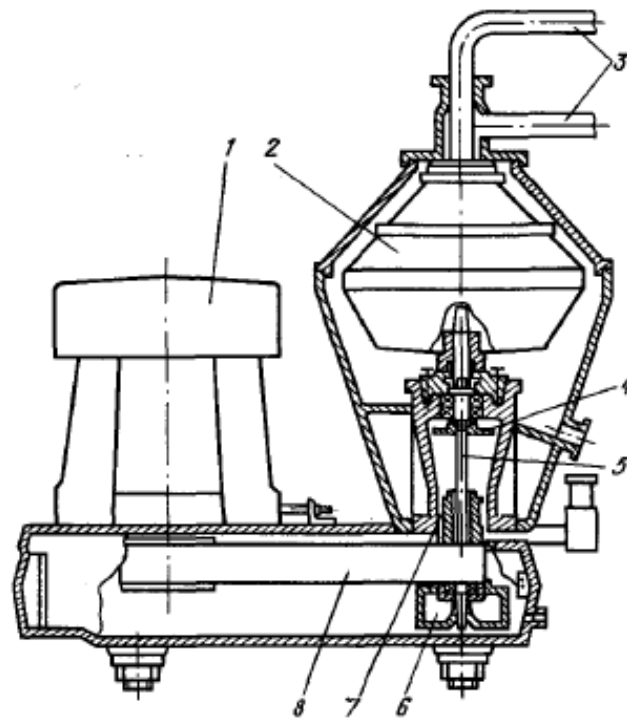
Сепаратор фірми «Альфа-Лаваль»: 1-електродвигун; 2-барабан; 3-патрубки; 4-розпилювач; 5-вертикальний вал; 6-картер; 7-сопло; 8-пасова передача
